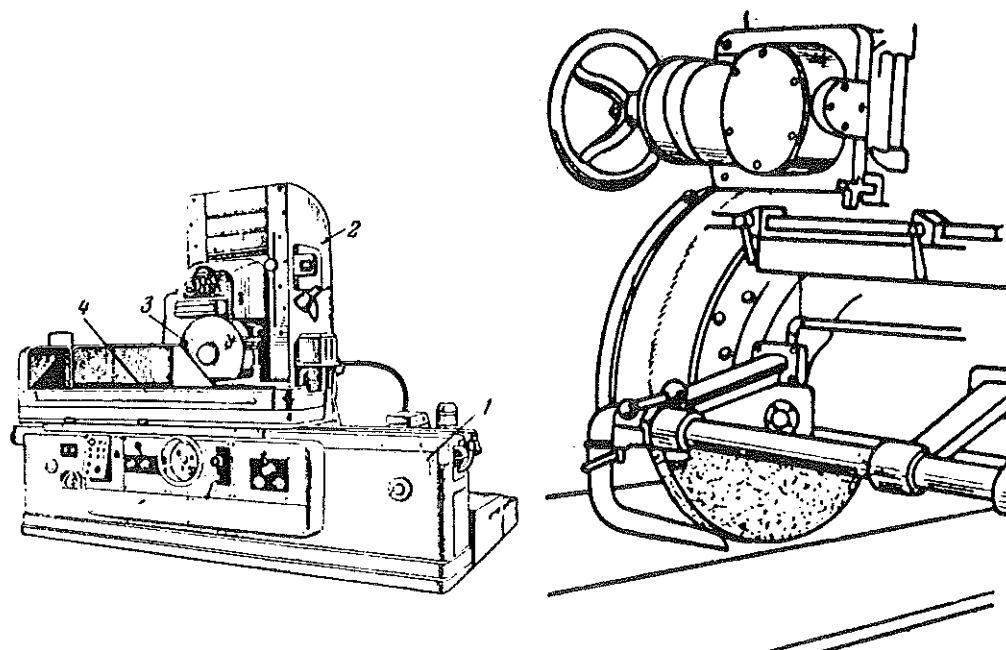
Retificadora frontal com mesa retangular de movimento alternado.
